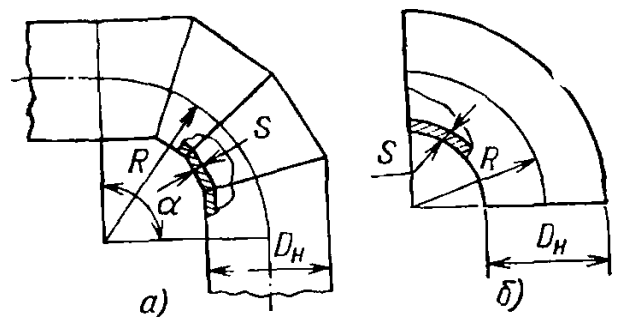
Типы отводов: а — секторный (сварной); б — штампованный
